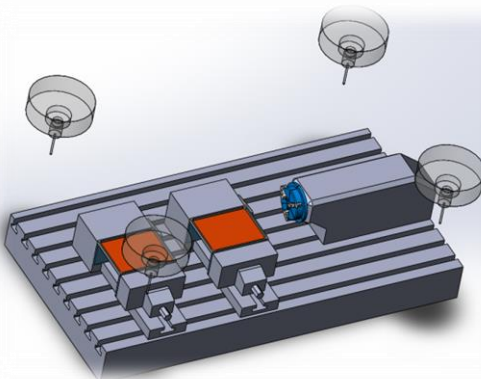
Детали с незафиксированной обрабатываемой поверхностью
